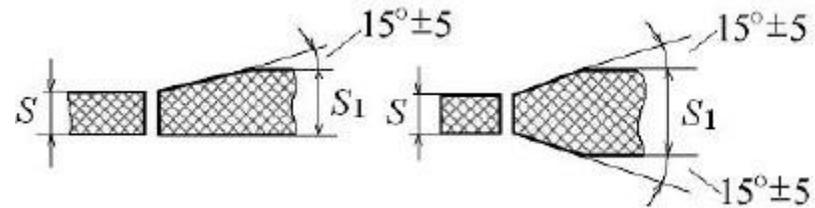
Подготовка кромок при сварке разнотолщинных материалов
